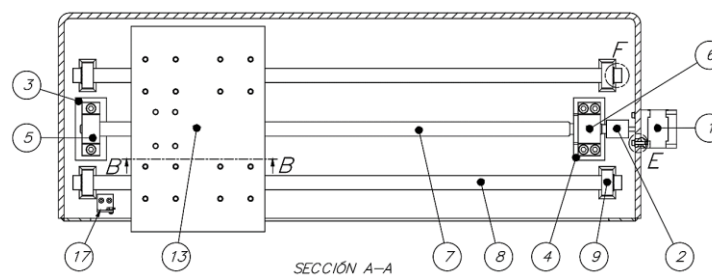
Desplazamiento X – Plano PE1.4.1-A2
